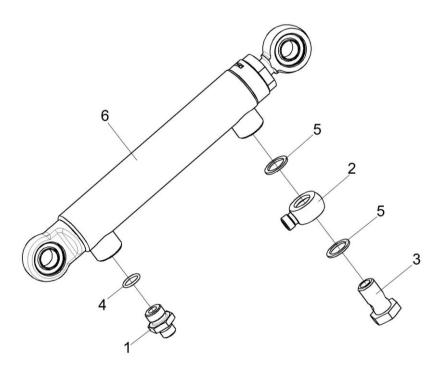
Гидроцилиндр КЗК-8-0602500
